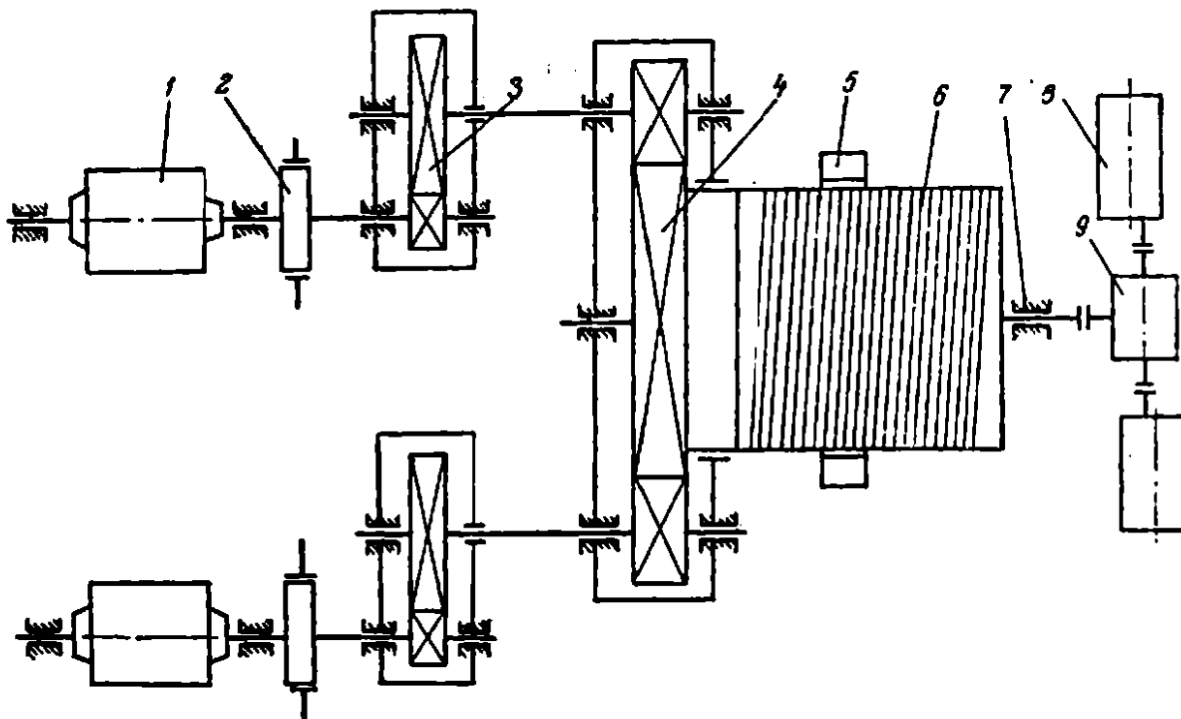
Кинематическая схема скиповой лебёдки С-22,5-210
